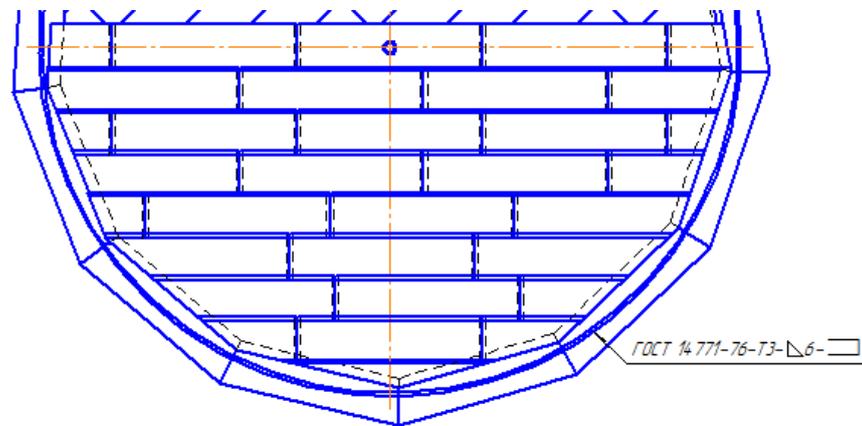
Сварка по дуговому контуру днища с окрайкой
